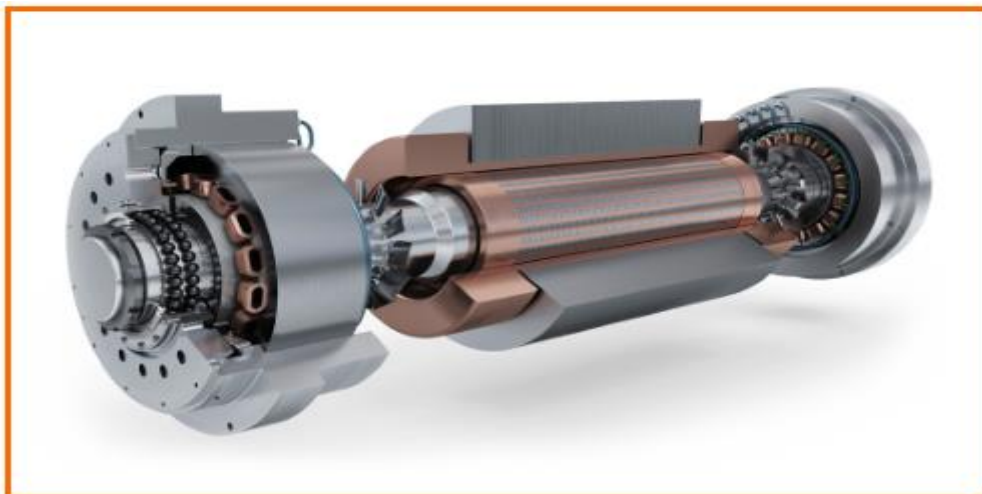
Турбодетандеры с магнитными подшипниками
